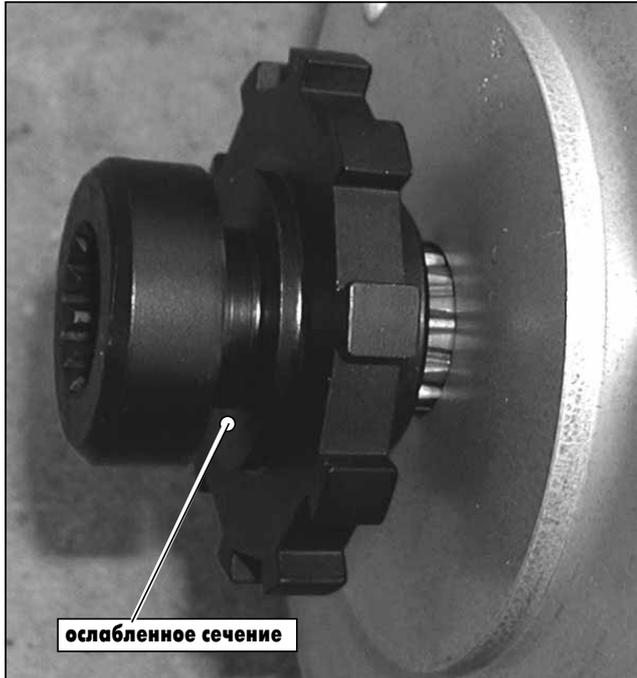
Резьбовые отверстия для крепления электродвигателя привода диска (соединительный элемент установлен)
